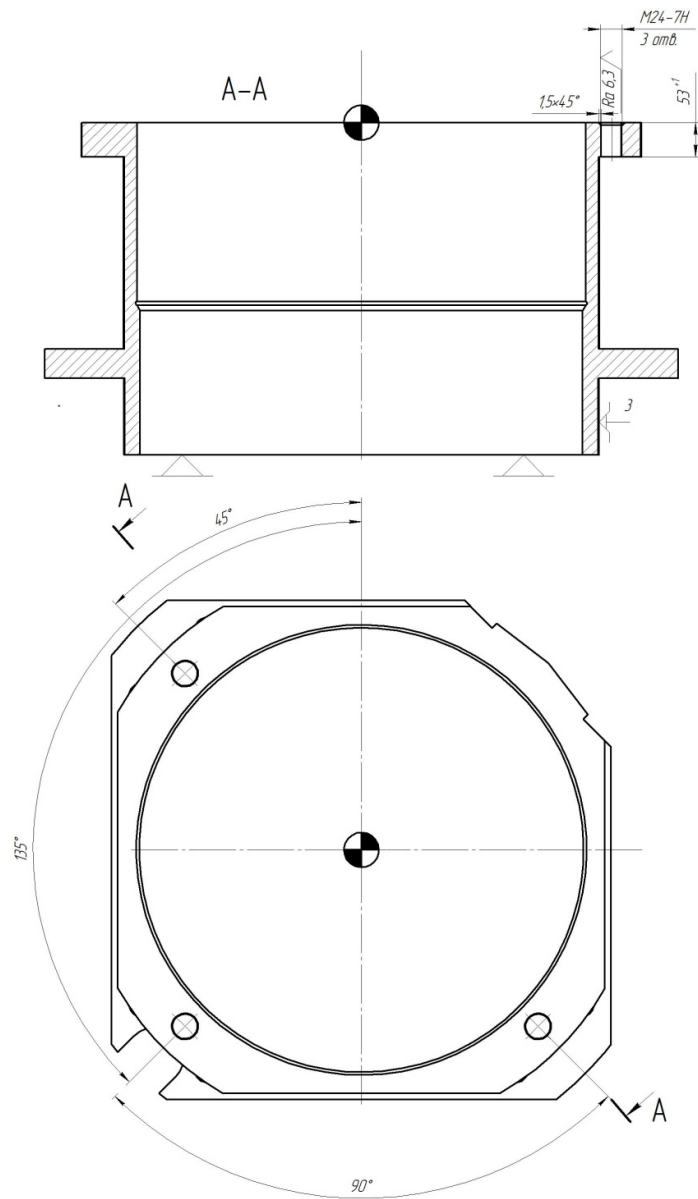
Фрезерна операція з ЧПК 025
